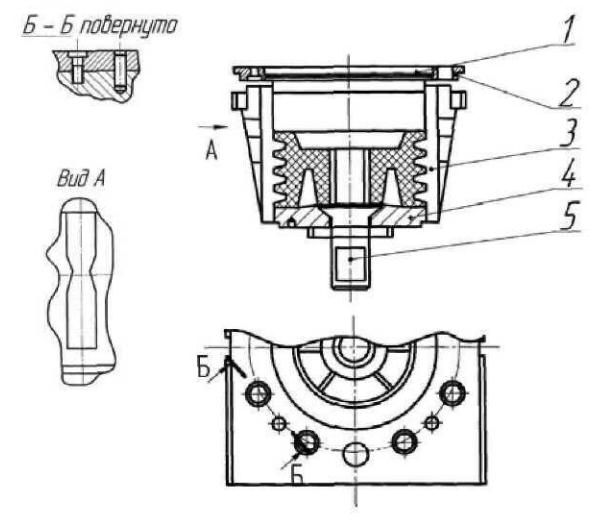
Пресс-форма для изготовления изделий методом прессования:
